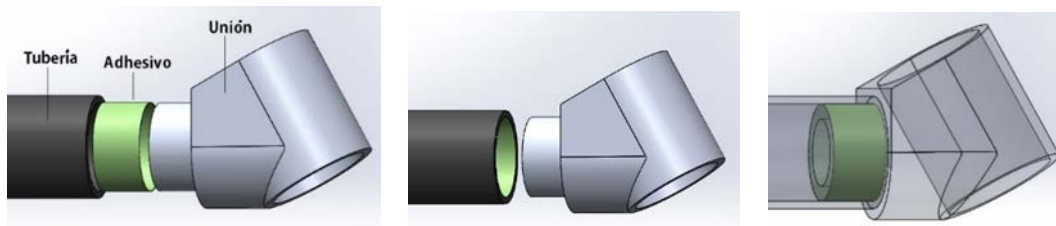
Ensamble de la tubería con adhesivo y el diseño de la unión
